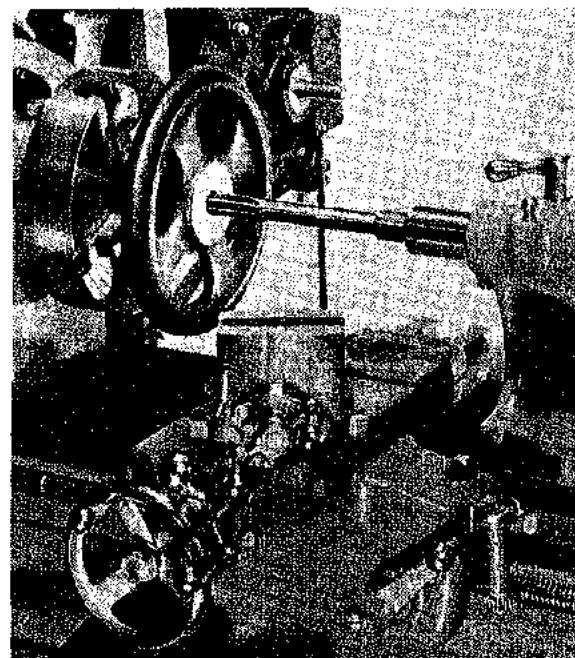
Escariador de mango cónico sujetado al husillo del contracabezal (Sheldon Machine Co., Inc.)
